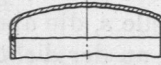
Stumpfe Schweißung an einem Boden.
